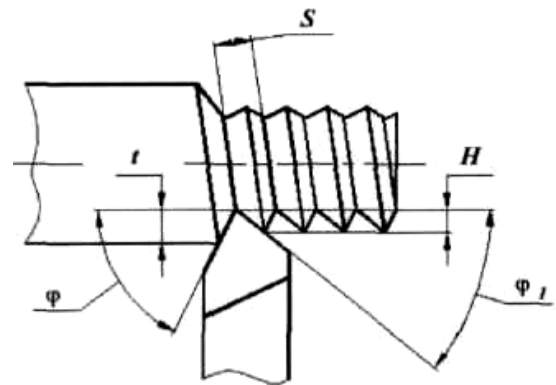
Залишковий переріз шару, що зрізується, на оброблюваній поверхні
